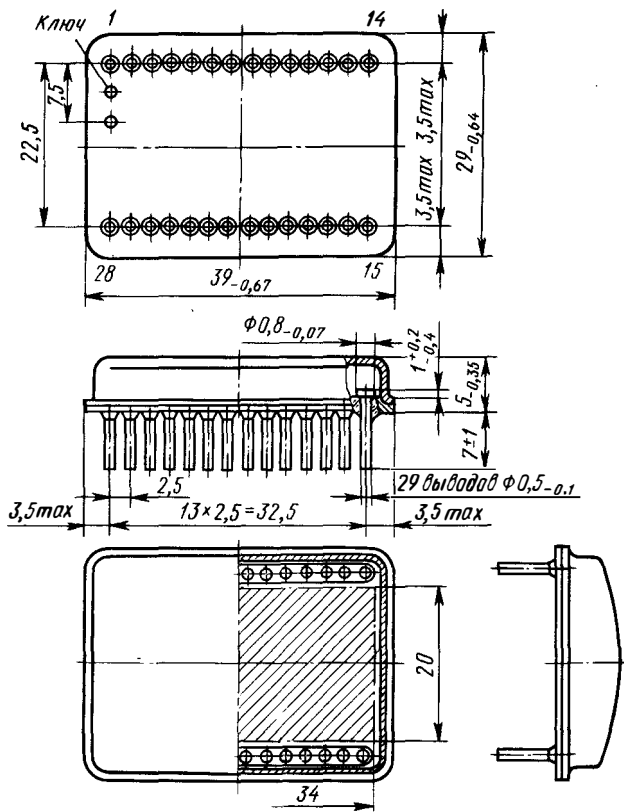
Металлостеклянный корпус типа 1210 (157.29-1)
